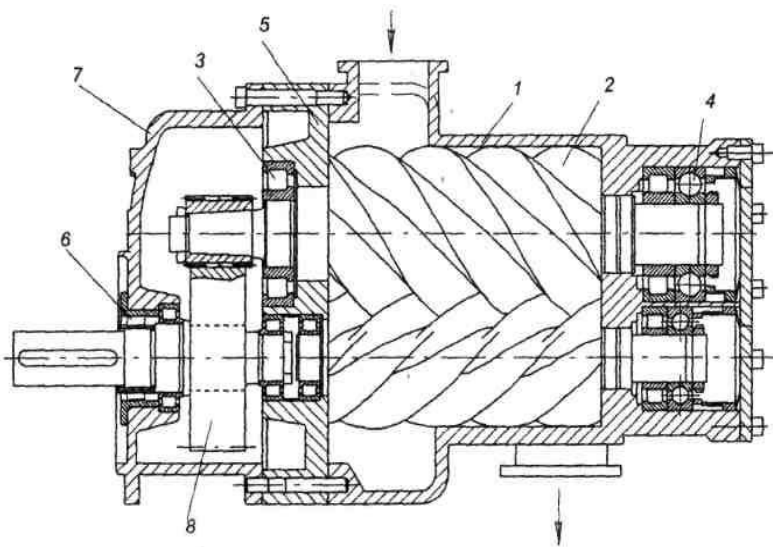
Гвинтовий компресор CF180G фірми GHH-Rand:
